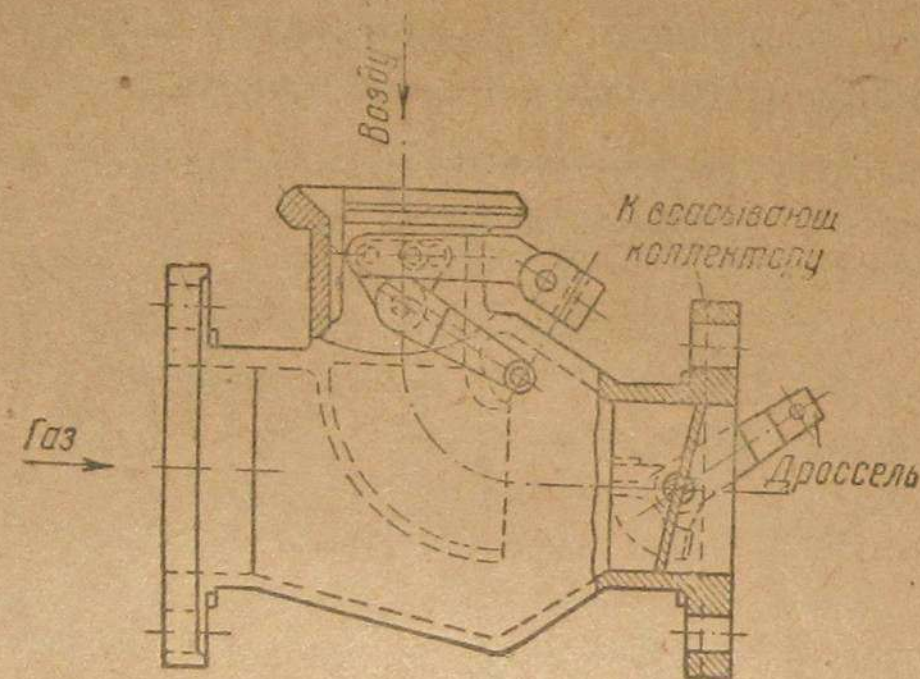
Общий вид смесителя газа двигателя ЗИС-21
